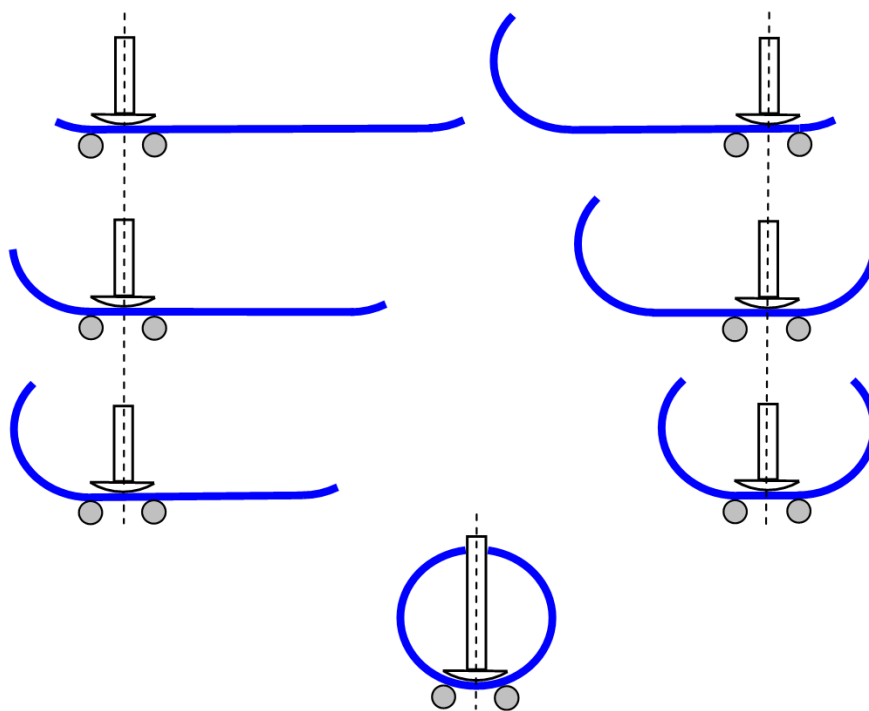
Гибка стальной заготовки на трубоформовочном прессе
